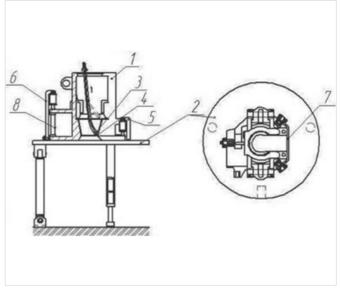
Схема установки и закрепления корпуса спайдера под наплавку. 1— корпус спайдера, 2— стол для наплавки, 3— сварочная головка, 4— наплавляемая поверхность, 5— пневматические прижимы без откидного механизма, 6— пневматический прижим с откидным механизмом, 7— установочный упор, 8— распорка
